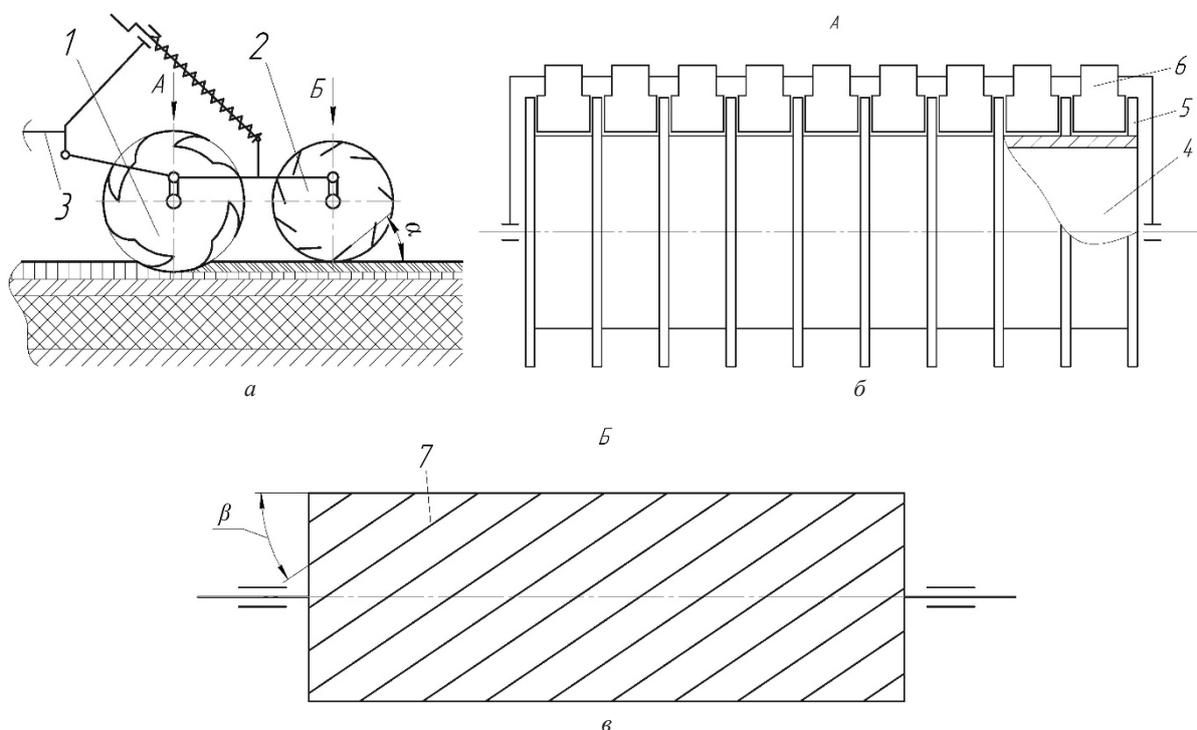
Схема блока прикатывающих катков: *a* – вид сбоку; *б* – вид А; *в* – вид Б; 1 – опорно-прикатывающий каток; 2 – мульчирующий каток; 3 – рама; 4 – цилиндр; 5 – зубчатые диски; 6 – чистики; 7 – планка
